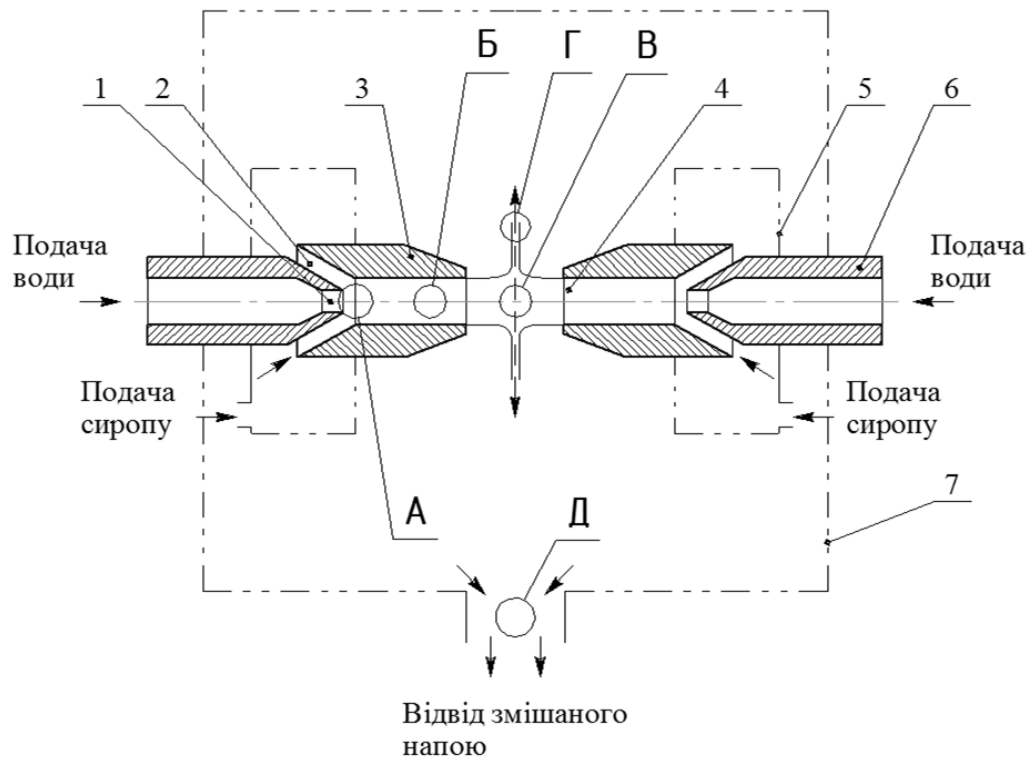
Схема протитечійно-струминного змішувача рідин: 1 – робоче сопло; 2 – приймальна камера; 3 – камера змішування; 4 – сопло камери змішування; 5 – камера подачі сиропу; 6 – робочий патрубок; 7 – камера збору рідини. А, Б, В, Г, Д – зони змішування.
